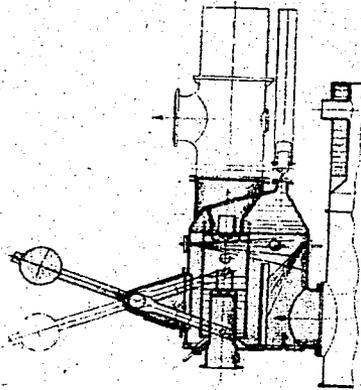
Umschaltventil zum Umstellen des Gaserzeugers auf Stillstand.
